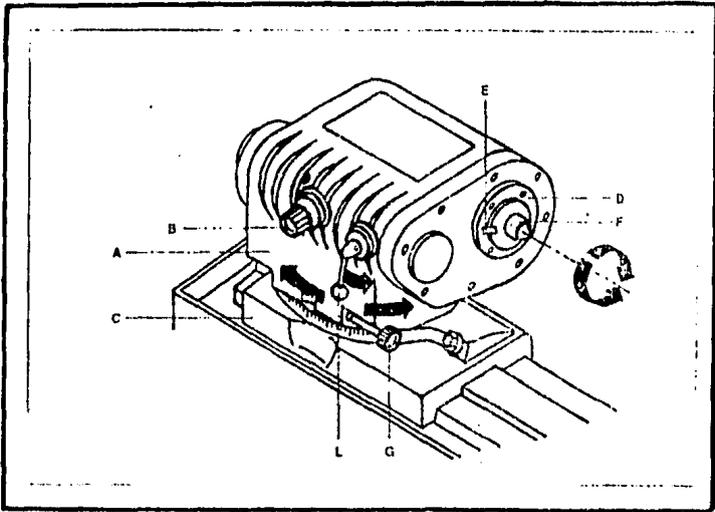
Cabezal portapiezas de una rectificadora cilíndrica para exteriores.
